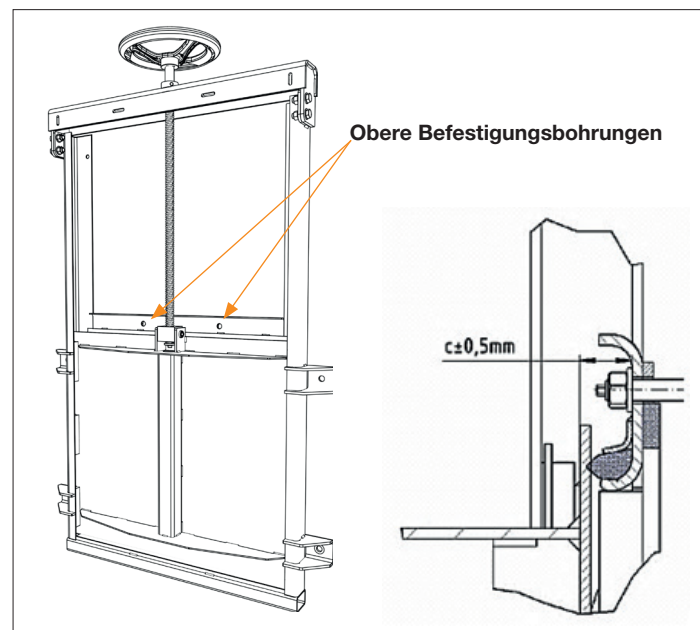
Montage Ankerstangen für obere Befestigungsbohrung
